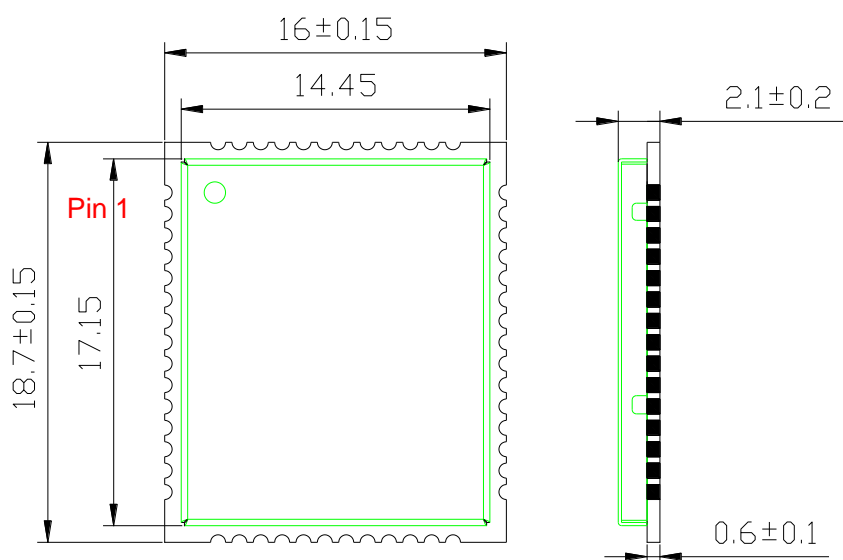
BC20-QuecOpen 俯视及侧视图尺寸
